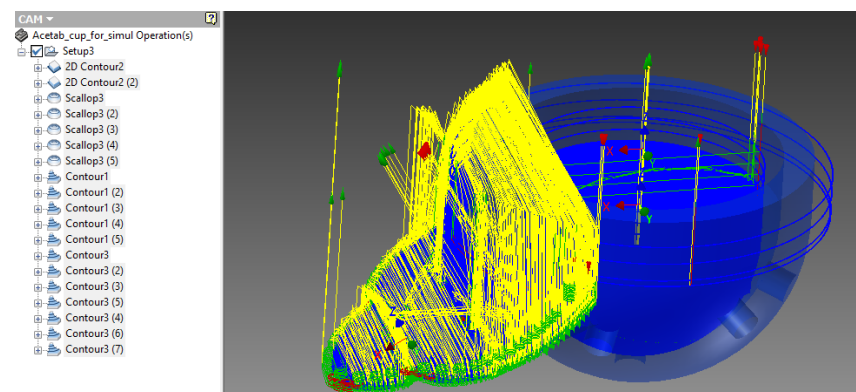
Після підготовки бази і обробки всіх поверхонь перевстановлюємо заготовку іншим боком в цанговий зажим
